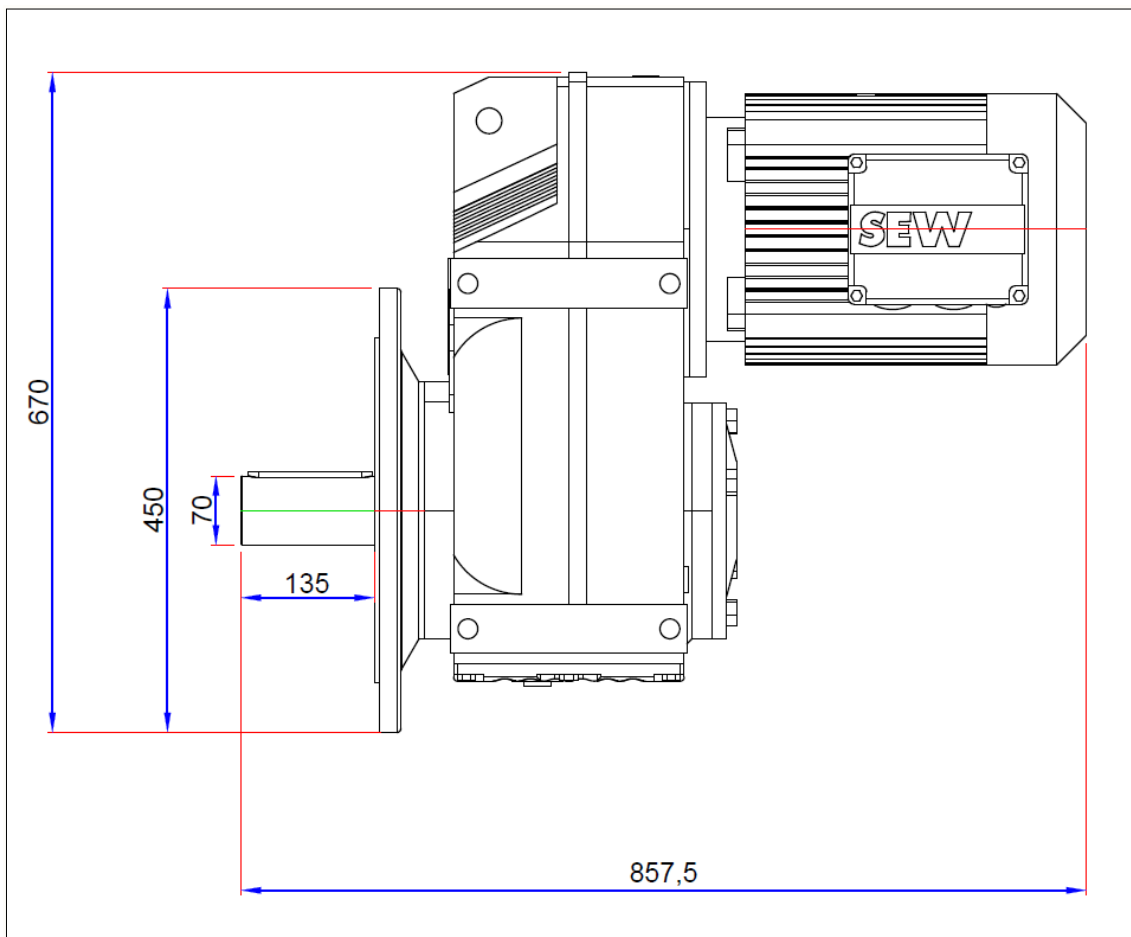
Vista anterior y dimensiones de motorreductor de engranajes helicoidales y ejes paralelos, línea F.
